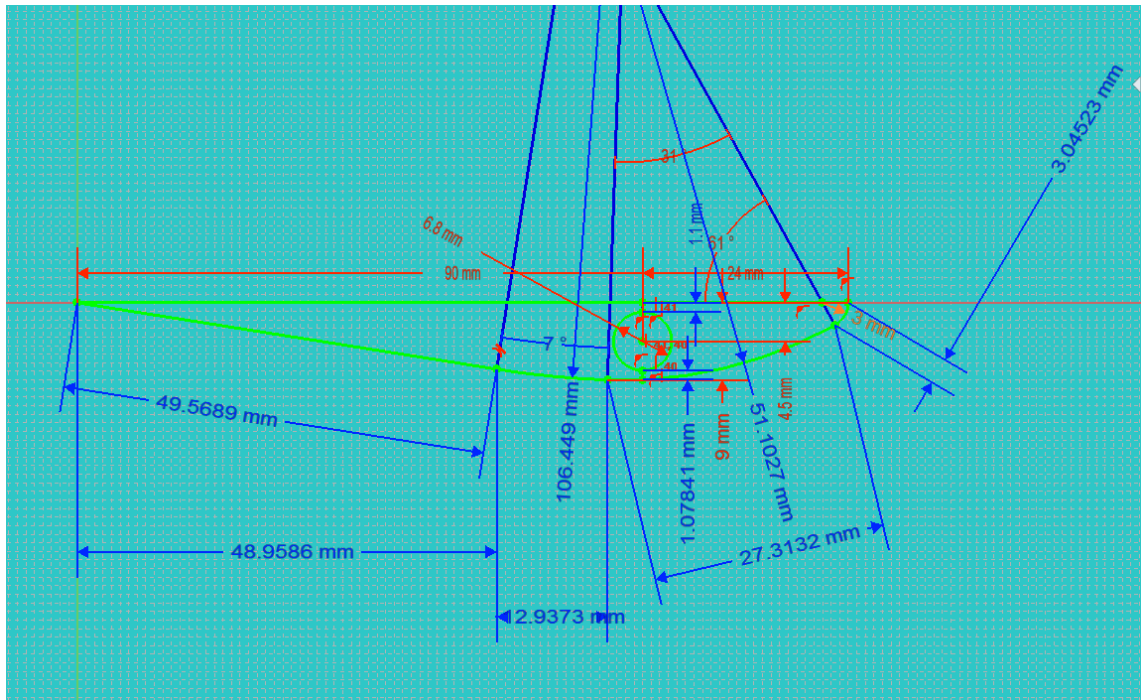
Plano de medidas pieza de adaptación. Fuente Propia.
